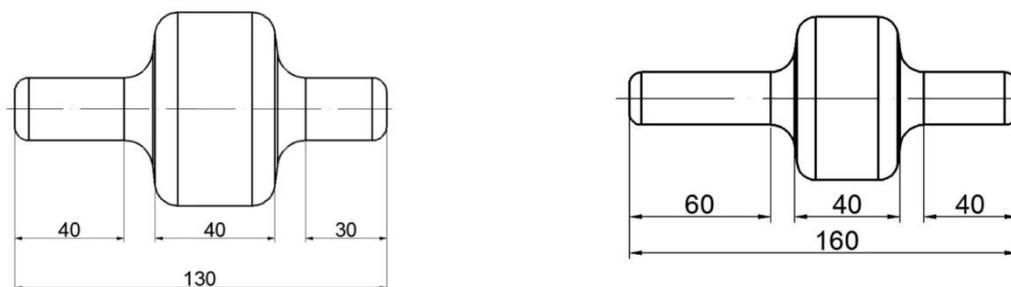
Штамповка из заготовок, полученных поперечно-клиновой прокаткой
